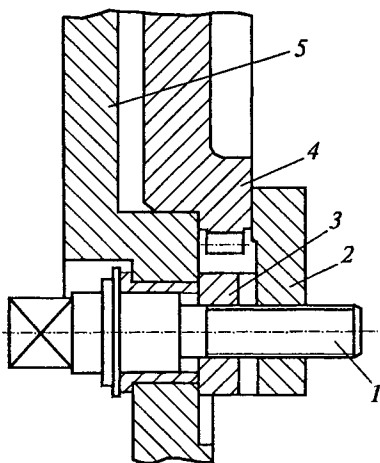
Стопорное устройство траверсы электродвигателя ДТК-800КЭ:
